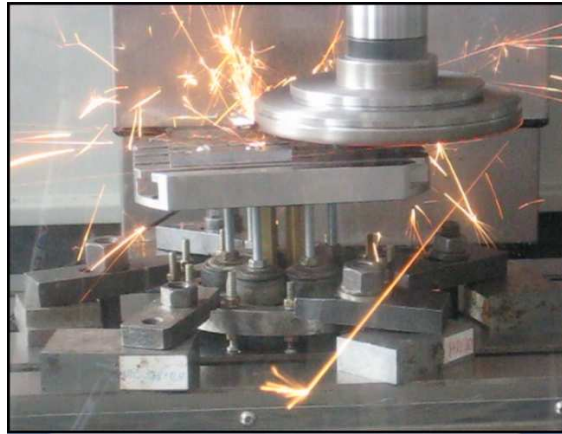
Срыв капель жидкого металла с периферийной части инструмента
